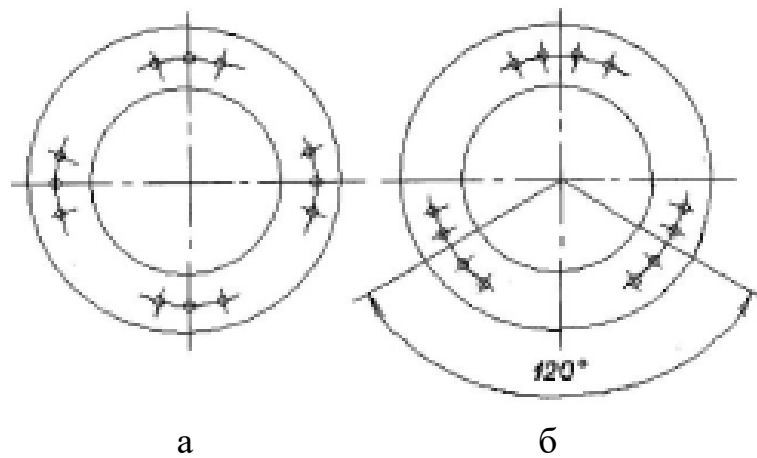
Схемы крепления корпуса конвертера в опорном кольце
